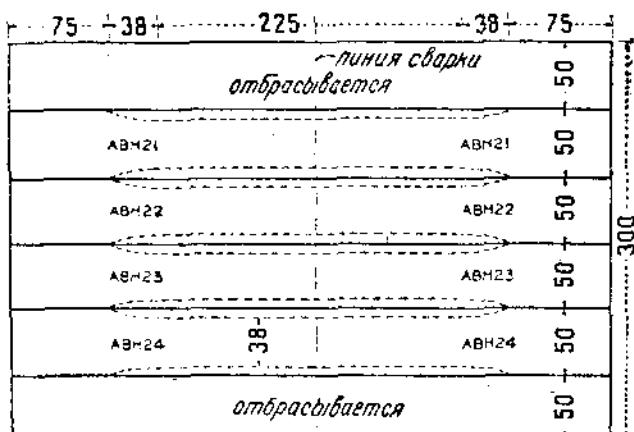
Разреака пробных планок на образцы для лабораторного испытания.
